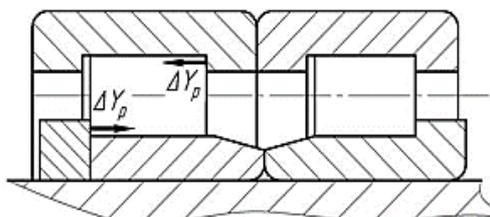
Схема передачи рамной силы цилиндрическим подшипникам
